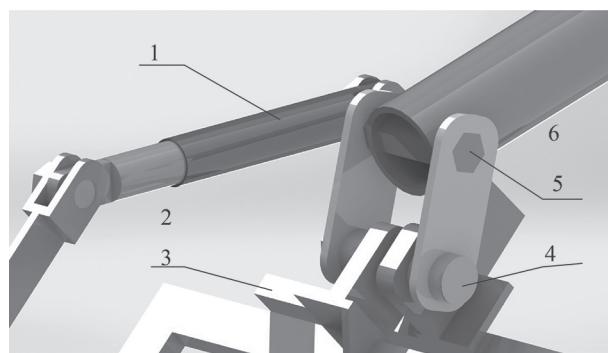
Грейферный захват для леса фронтального погрузчика (вид сбоку):
